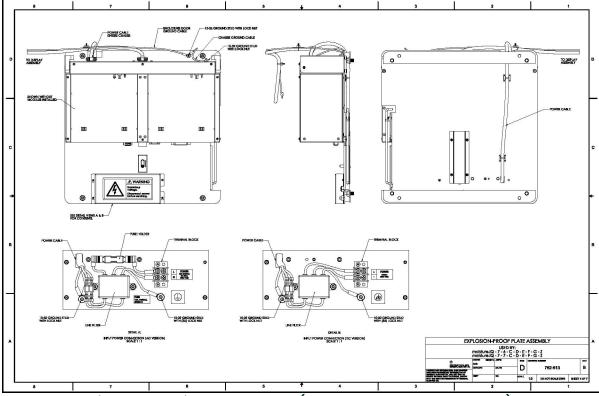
Conjunto de placas XP (desenho 752-513\_revB, SH 4 de 5)
